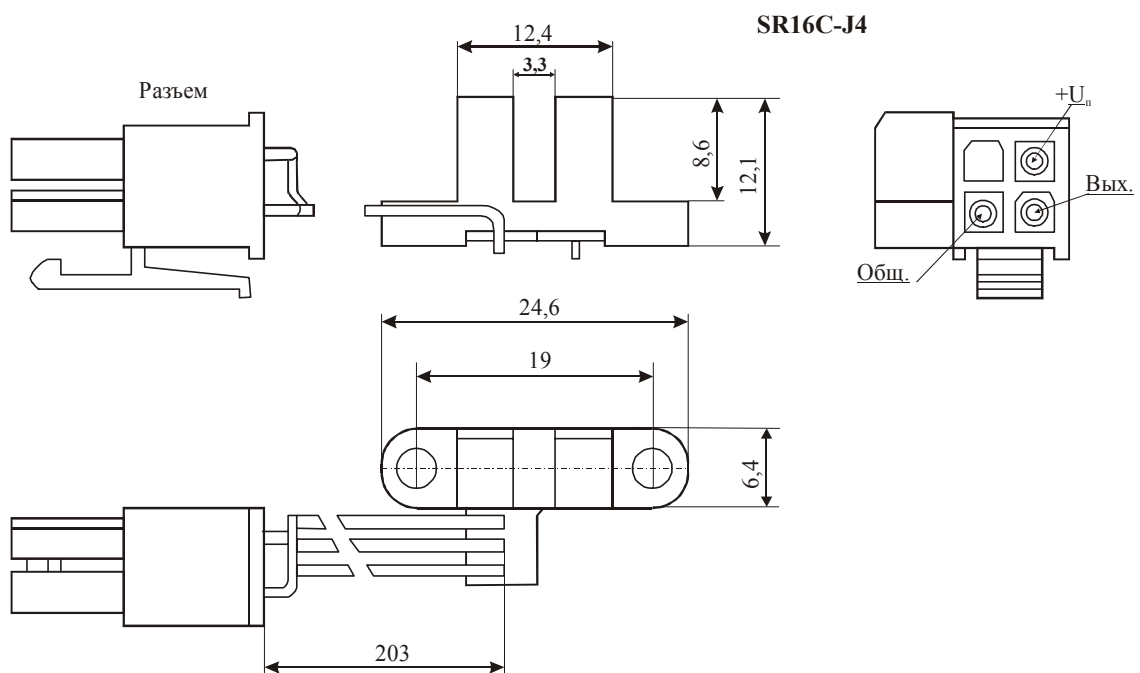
Внешний вид и габаритные размеры ЦМД типа SR16C-J4
